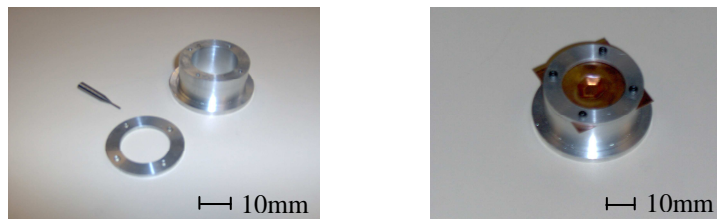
Equipement expérimental utilisé pour le formage incrémental
